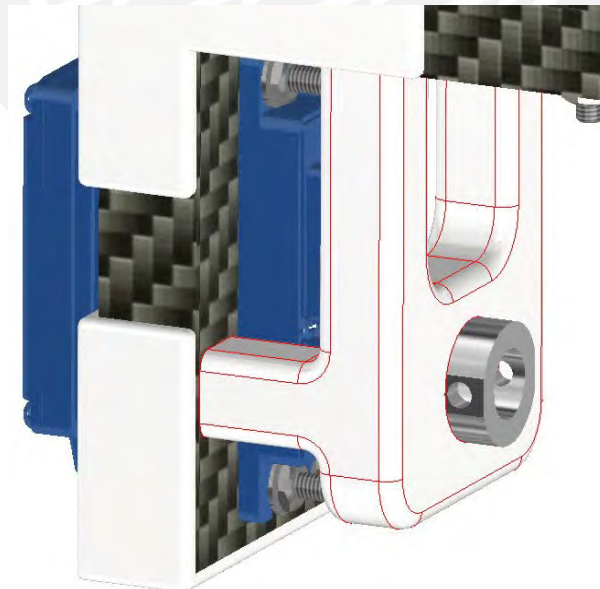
Pieza de soporte de la parte inferior del módulo. Fuente propia
